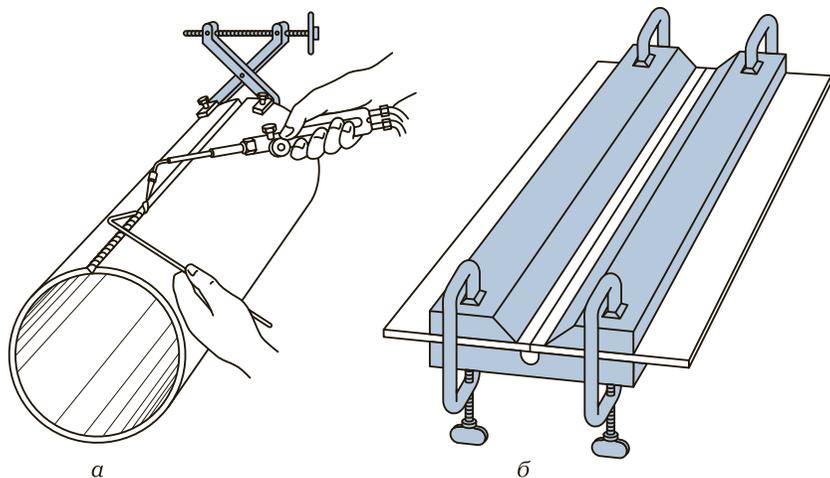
Зажимные приспособления для сварки с переменным (а) и постоянным (б) зазором
